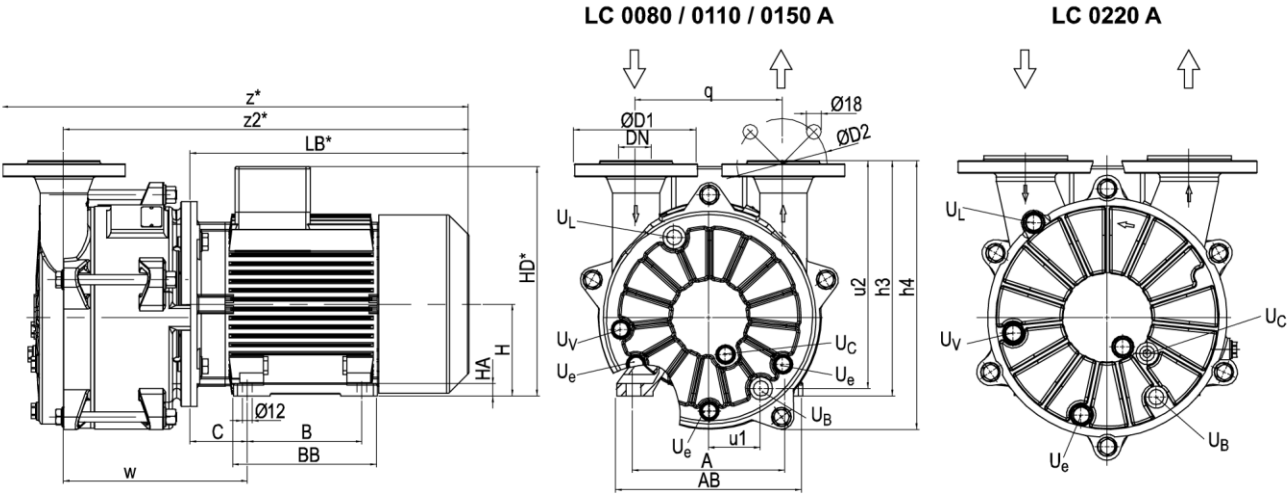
Размерный чертеж LC0080 A – LC0220 A
